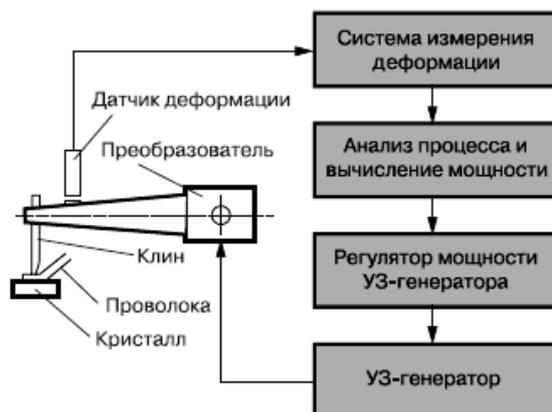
Схема системы контроля процесса сварки алюминиевой проволокой [4]
